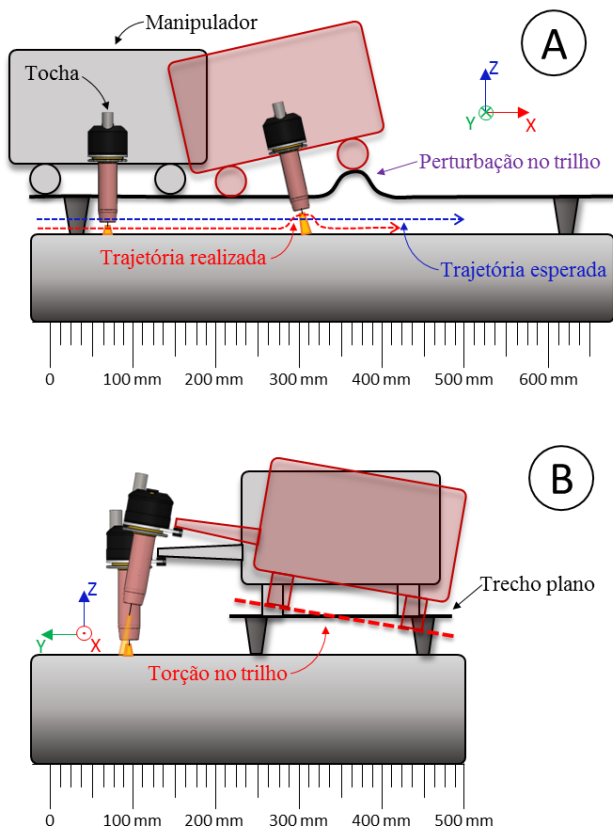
Representação do efeito das imperfeições do trilho sobre a posição do TCP da tocha de soldagem.
